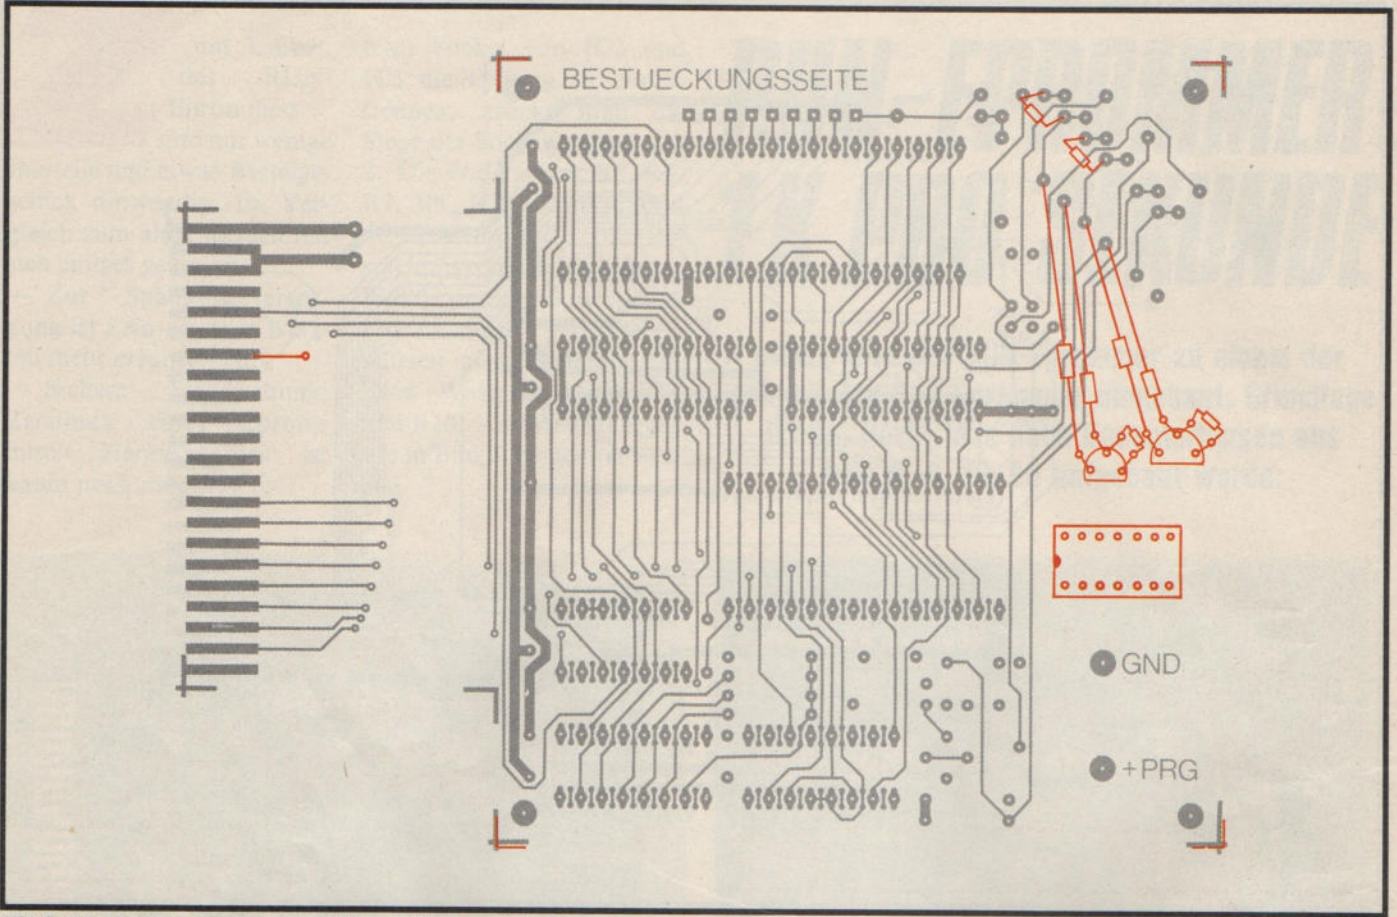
Die blau gekennzeichneten Löcher müssen gebohrt werden.
